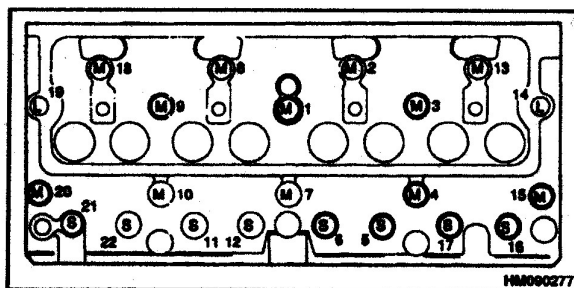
Последовательность подтяжки крышки цилиндра, четырехцилиндровые двигатели
